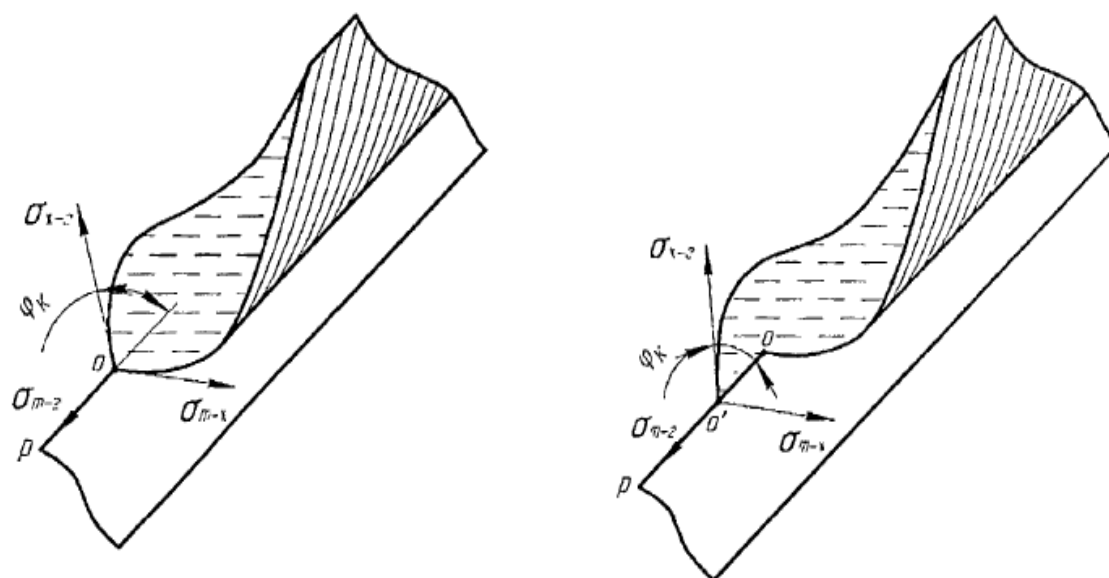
Удержание металла сварочной ванны за счет наличия фронта плавления в головной части сварочной ванны
